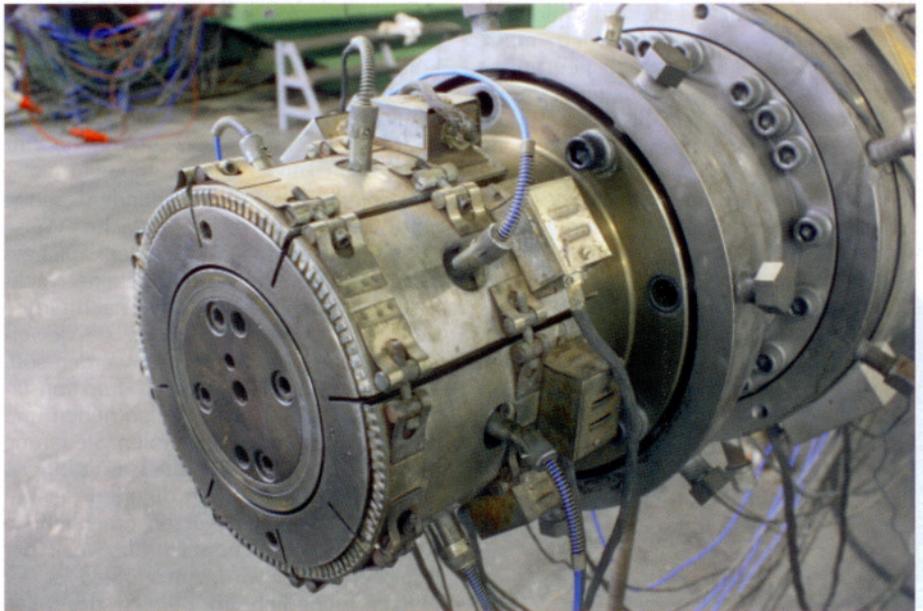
Mit einem elastischen Kippgelenk nachgerüsteter Rohkopf, mit dem kerngeschäumte PVC-Rohre hergestellt werden (Rohrdurchmesser 160 mm).
